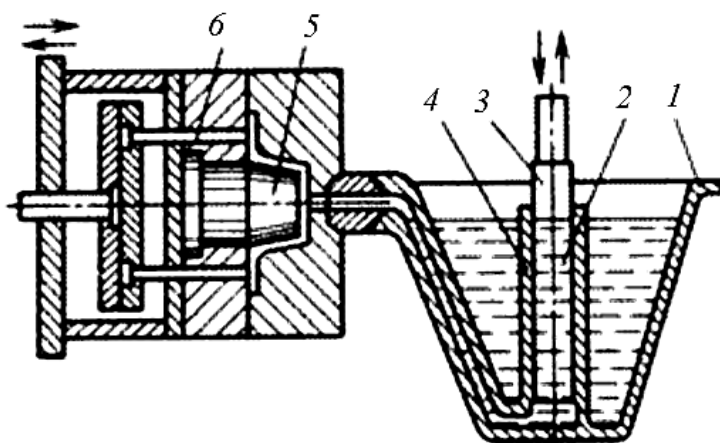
Схема изготовления отливки на машинах с горячей камерой прессования
